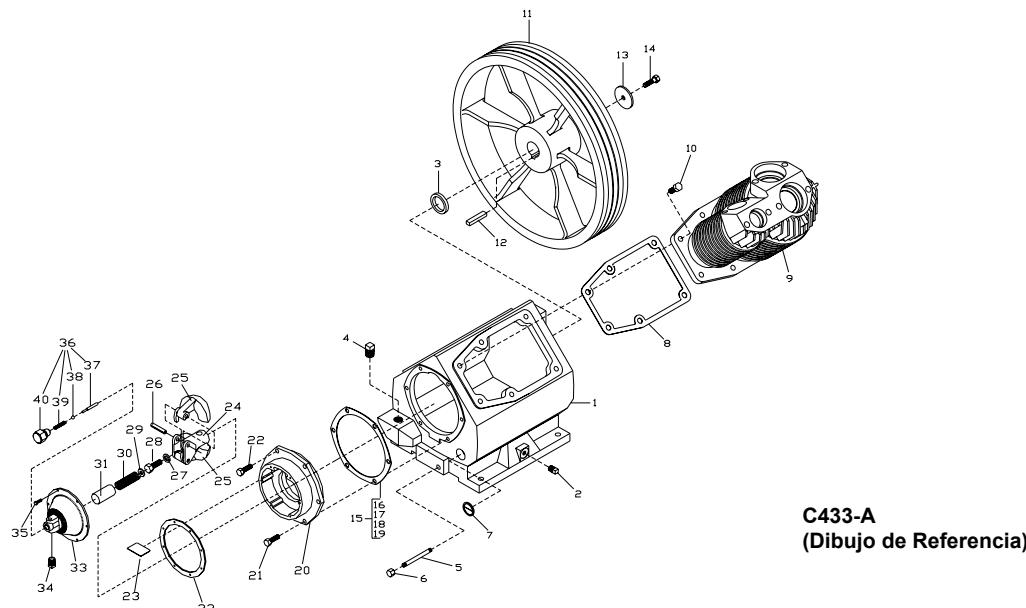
Ilustración de piezas de repuesto para conjuntos de volante, descargador centrífugo y carter
